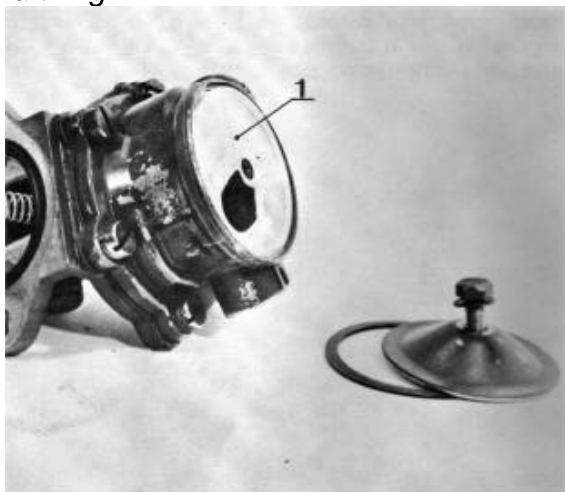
, sil i matarpumpen som ska rensas i samband med filterbyte, man skymtar den svarta o-ringen som tätar mot motorblocket längst till vänster i bilden.
